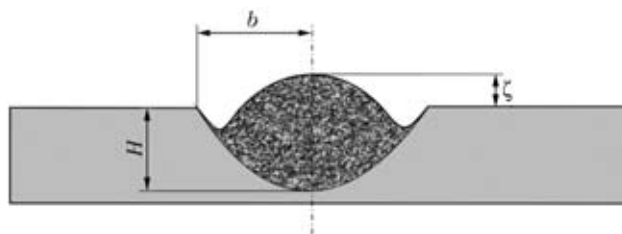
Обозначение параметров сечения сварочной ванны
